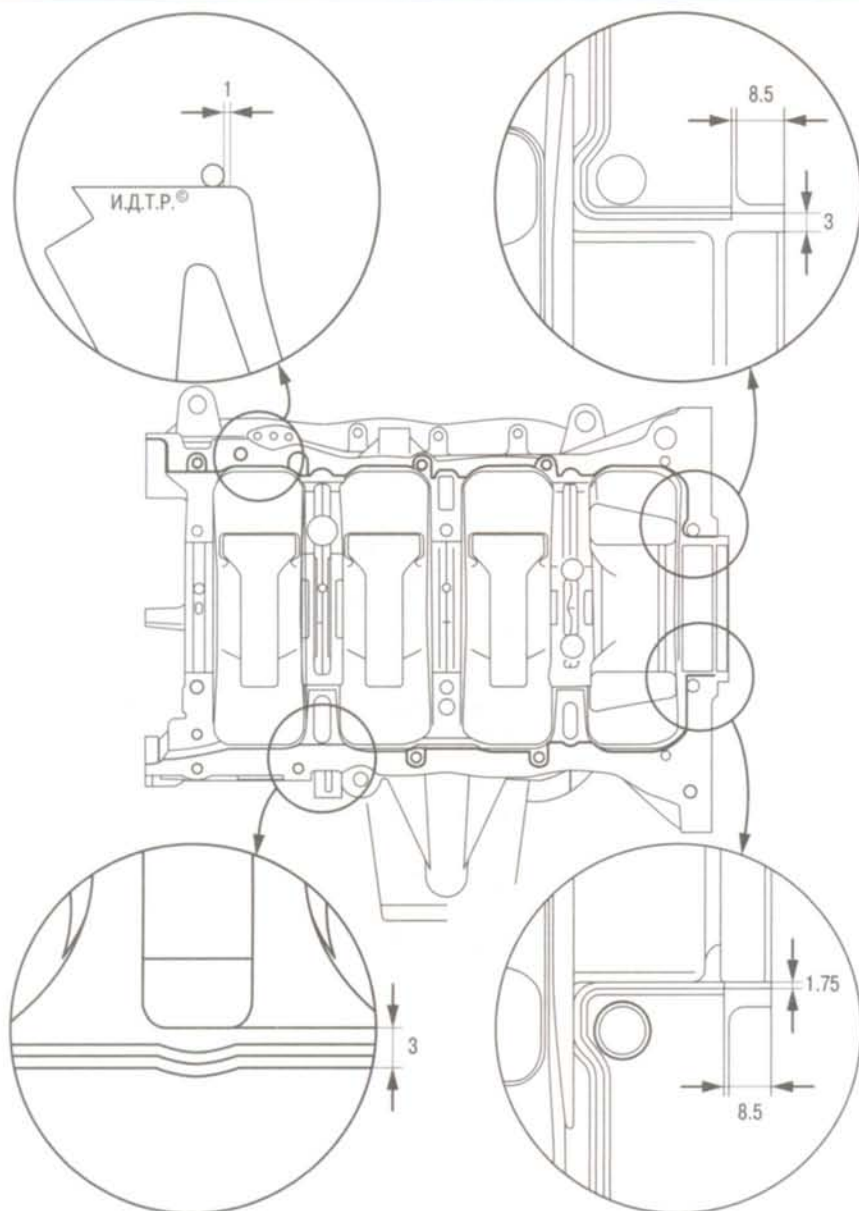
Схема нанесения герметика на привалочную поверхность головки блока цилиндров
